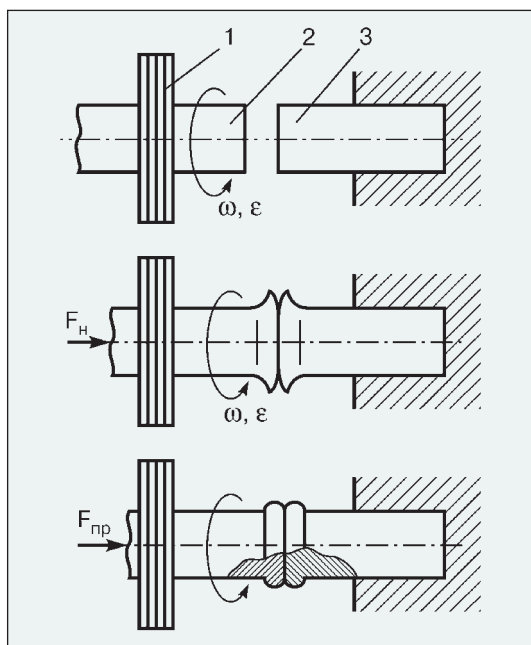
Схема инерционной сварки трением: 1 — маховик; 2, 3 — свариваемые заготовки
